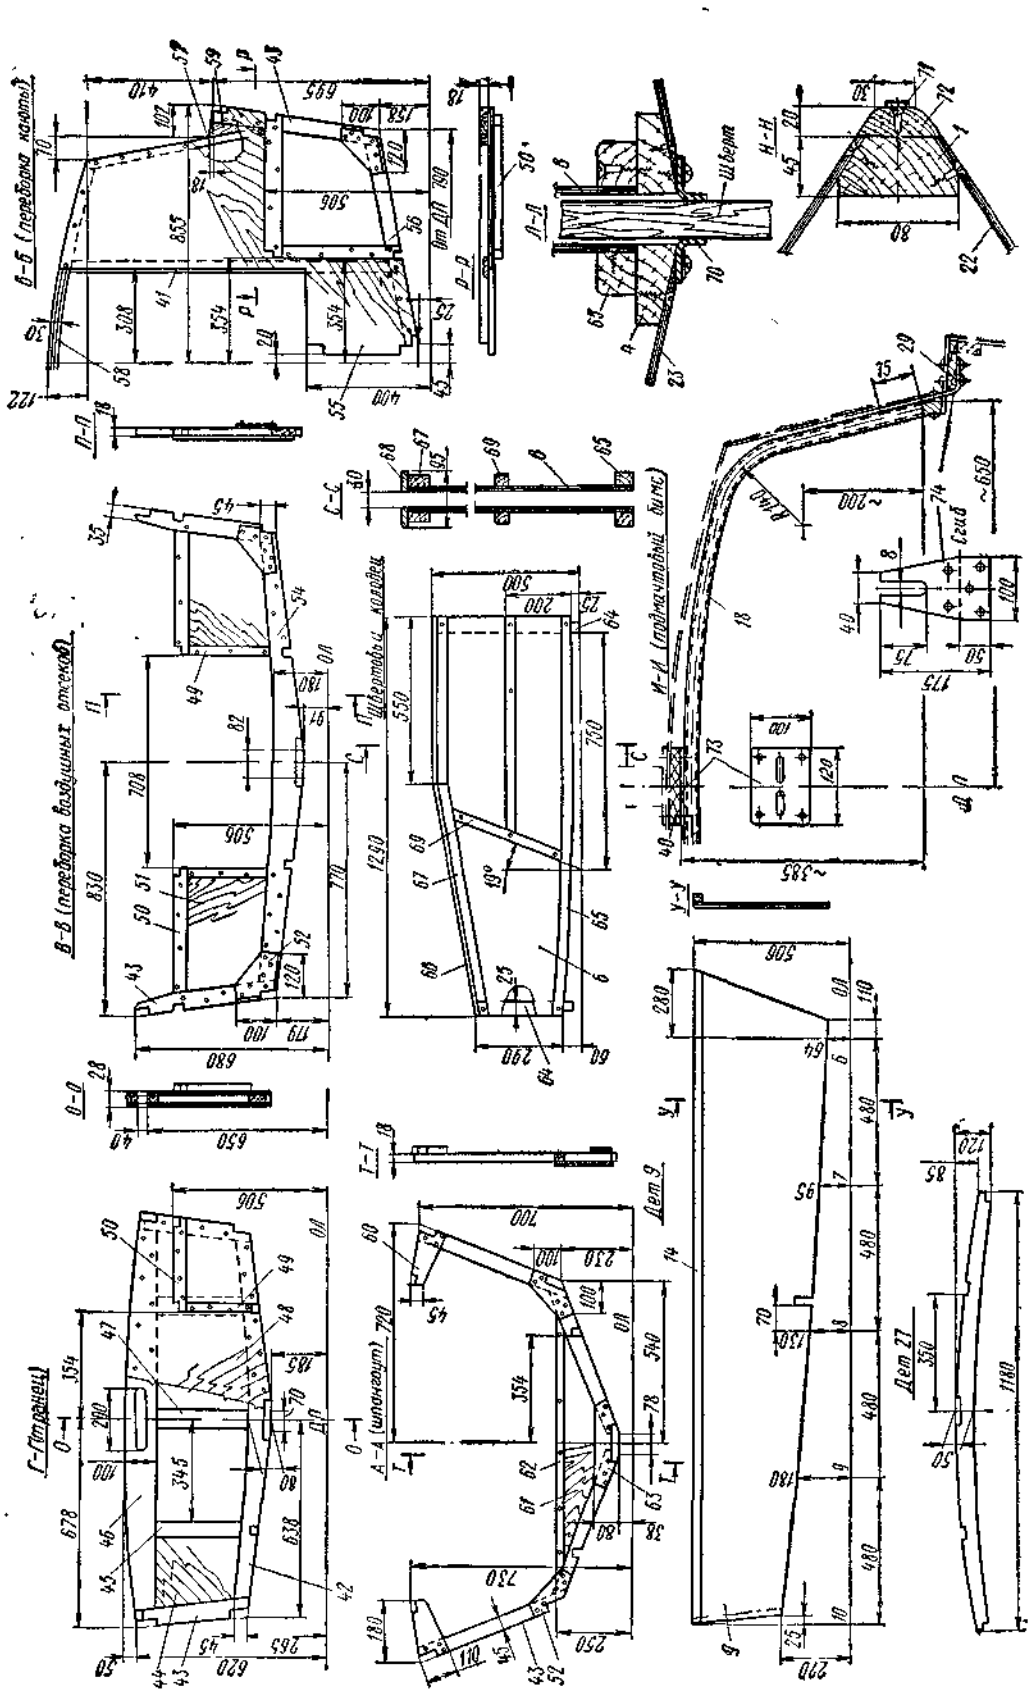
Сечения по шпангоутам и детали корпуса и рубки.
